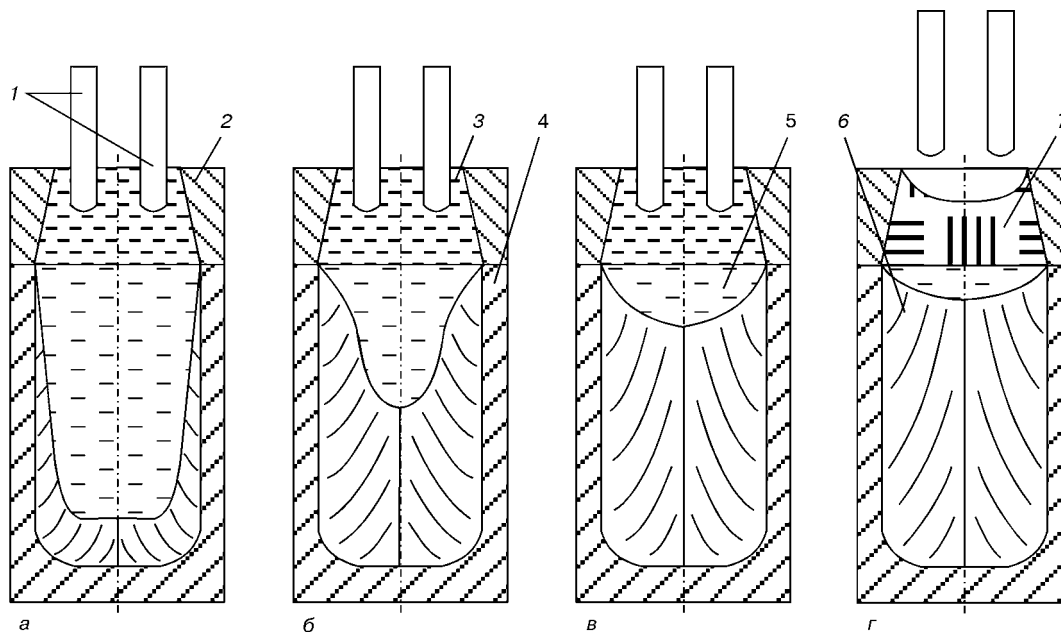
Схема электрошлакового обогрева головной части слитка: 1 — электроды; 2 — прибыльная надставка; 3 — жидкий шлак; 4 — изложница; 5 — жидкий металл; 6 — твердый металл; 7 — твердый шлак
